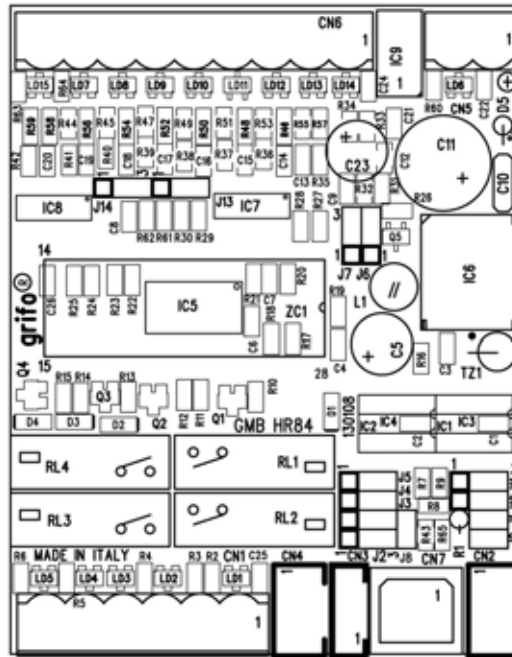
PIANTA COMPONENTI (LATO COMPONENTI)
